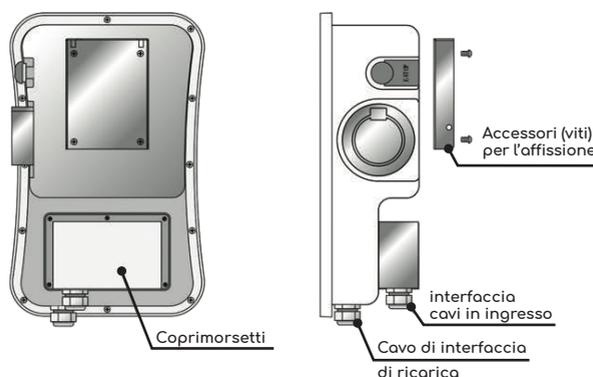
Fissare gli accessori per la sospensione a parete
